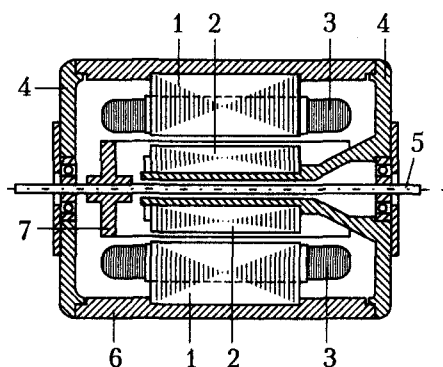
Устройство асинхронного исполнительного двигателя с полым немагнитным ротором: 1 — внешний статор; 2 — внутренний статор; 3 — обмотка; 4 — подшипниковые щиты; 5 — вал; 6 — корпус; 7 — полый ротор
